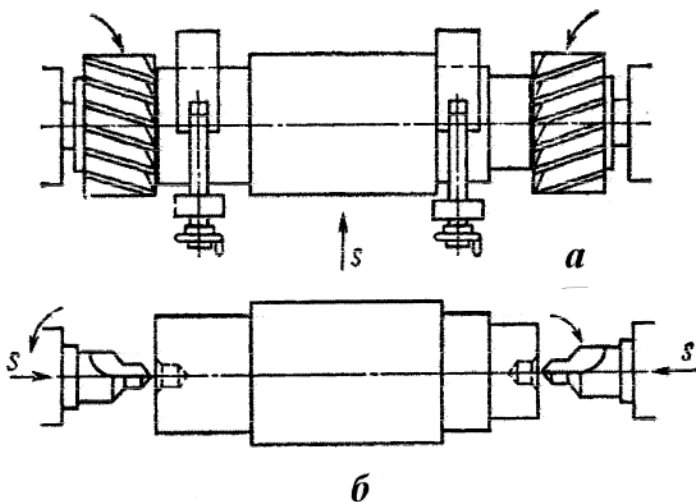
Схема обработки на фрезерно-центровальном станке.
